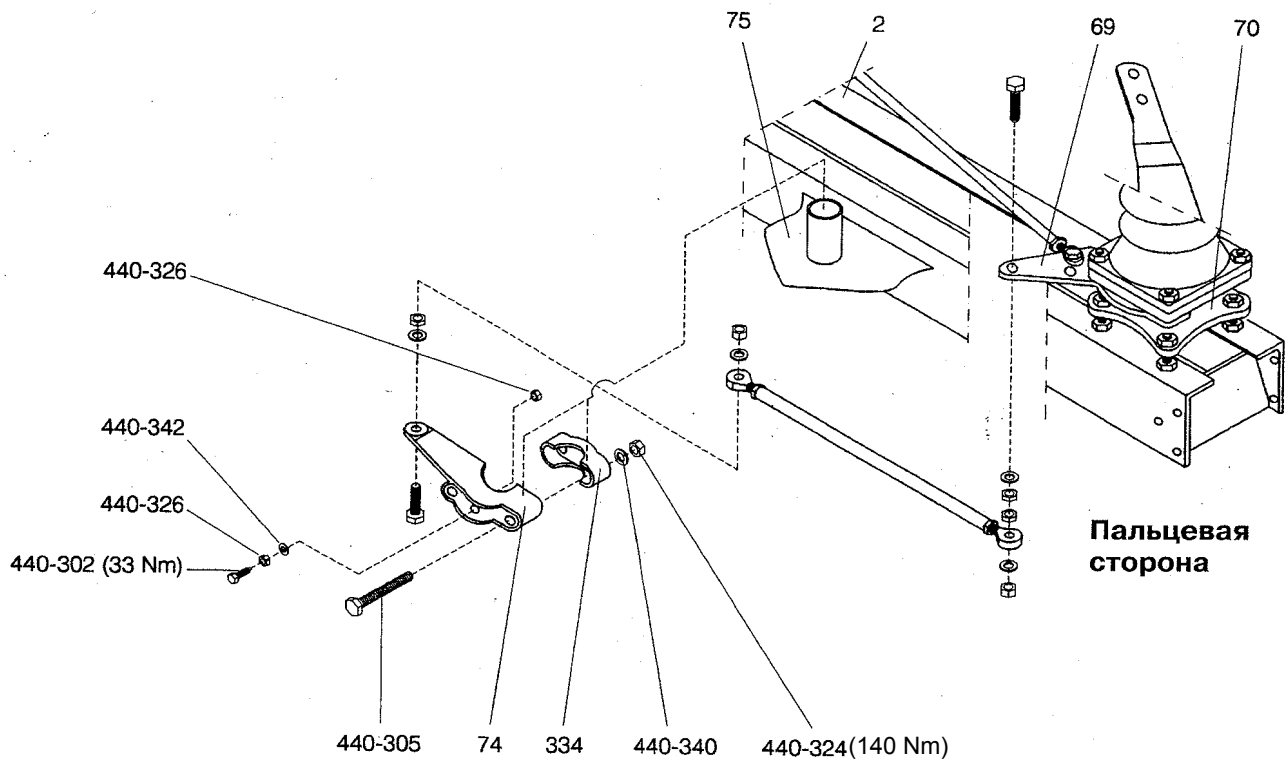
Установка приводного механизма разъединителя, непосредственно на основании полюса. Установка приводного рычага (74) при расположении приводного механизма разъединителя на стороне открывания
